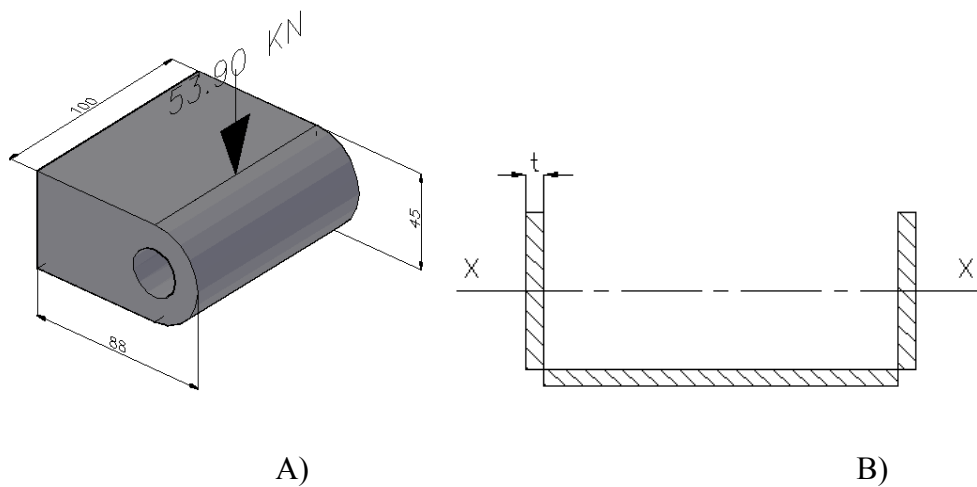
A) Fuerza actuante en bisagra. B) Sección del cordón de soldadura.
